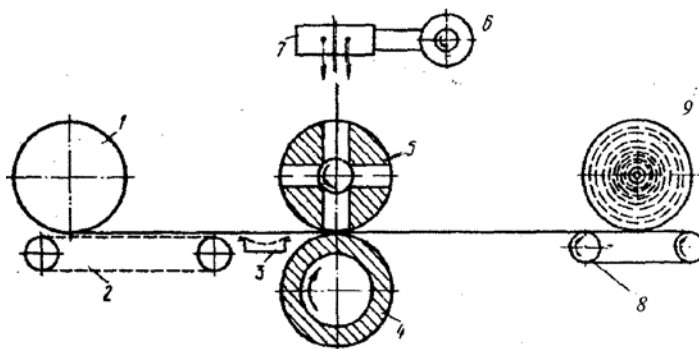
Схема установки для получения нетканых материалов точечной сваркой лучом лазера
